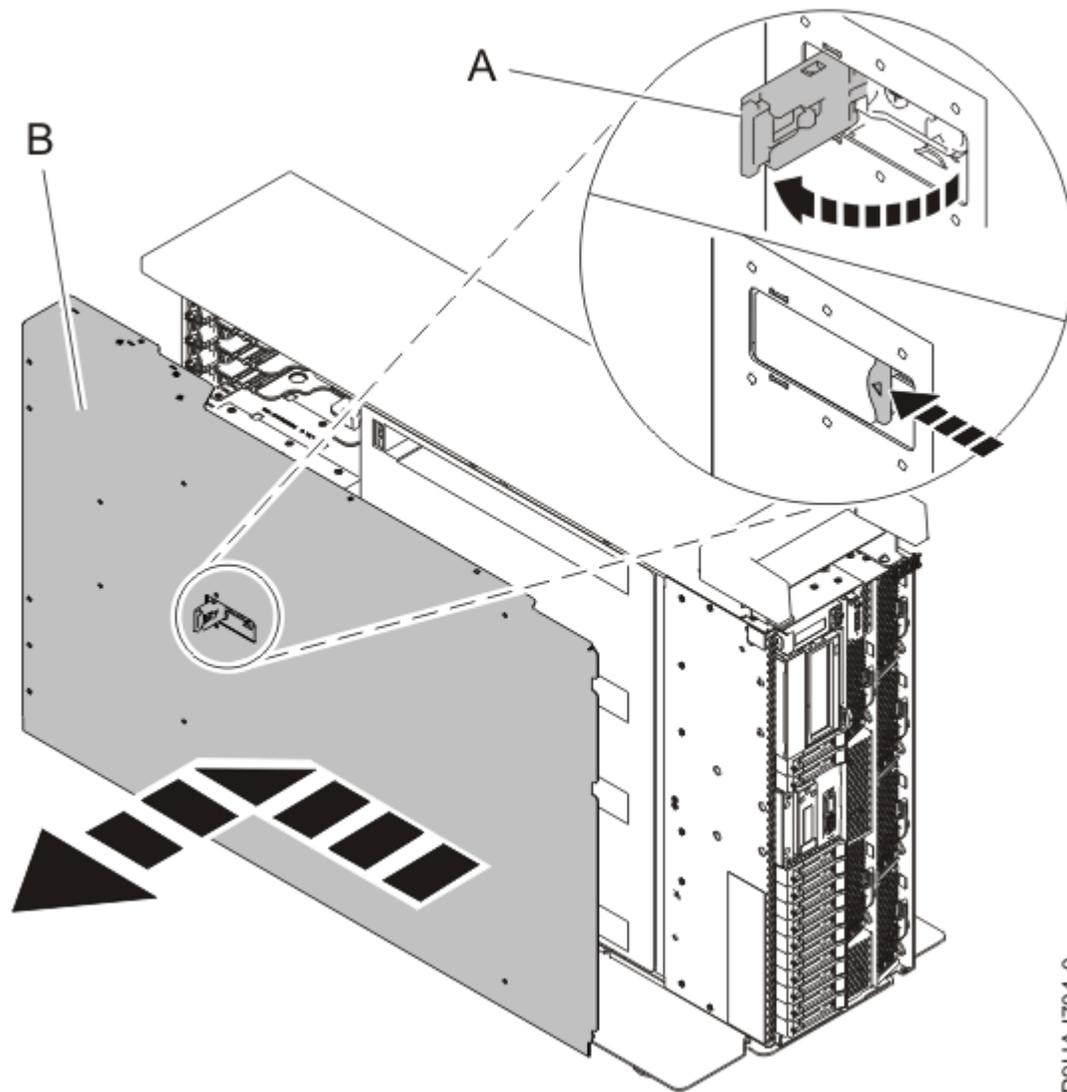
Extracción de la cubierta de acceso de servicio de un sistema montado en bastidor
